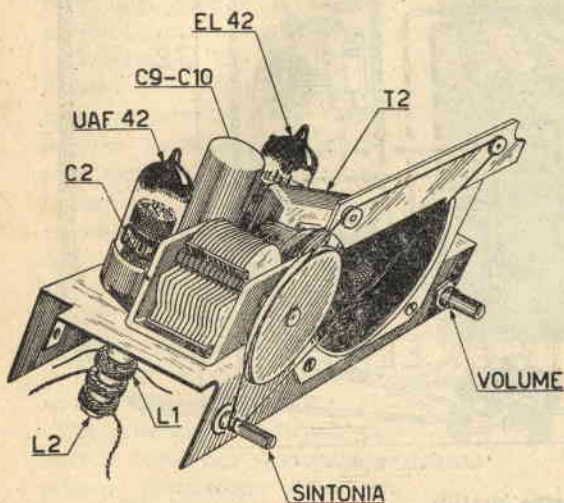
Vista prospettica laterale di sistemazione componenti sulla parte superiore del telaio.
